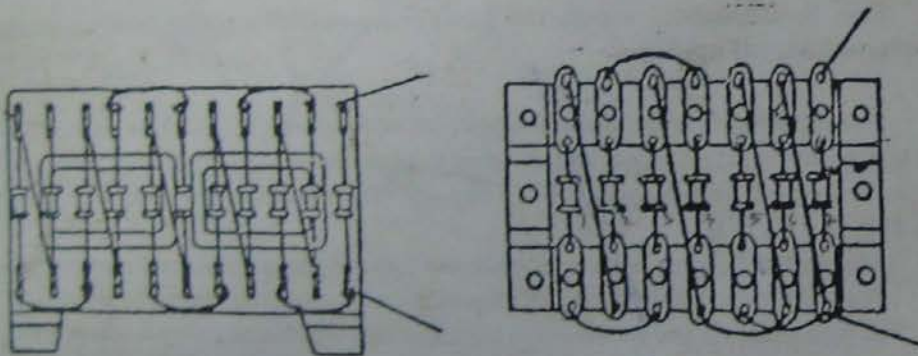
Примеры монтажных схем при монтаже элементов на опорных поверхностях монтажных плат
